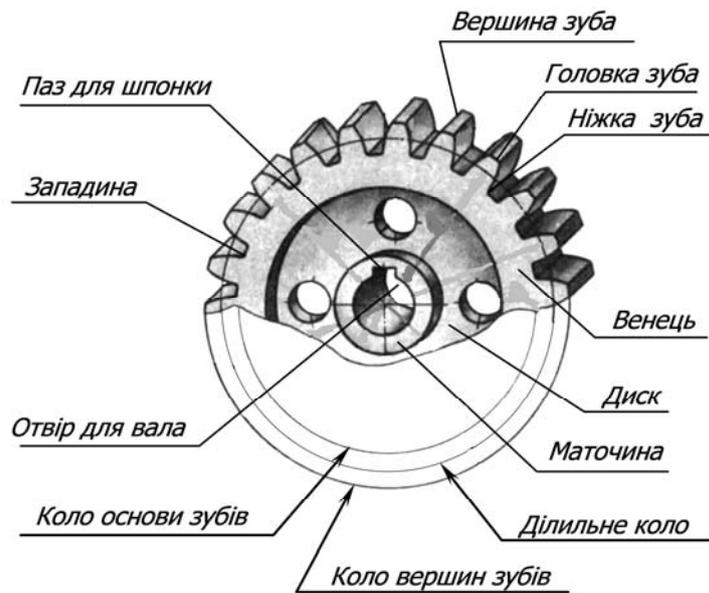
Загальний вигляд циліндричного зубчастого колеса
